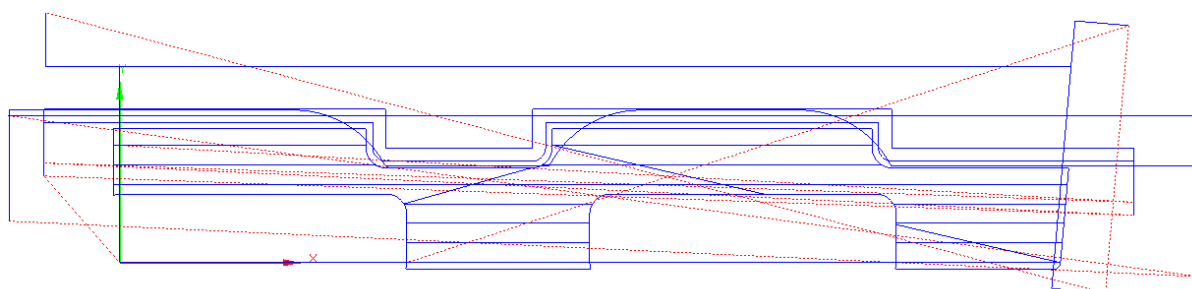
Hrubování tvaru součásti metodou VoluMill.
